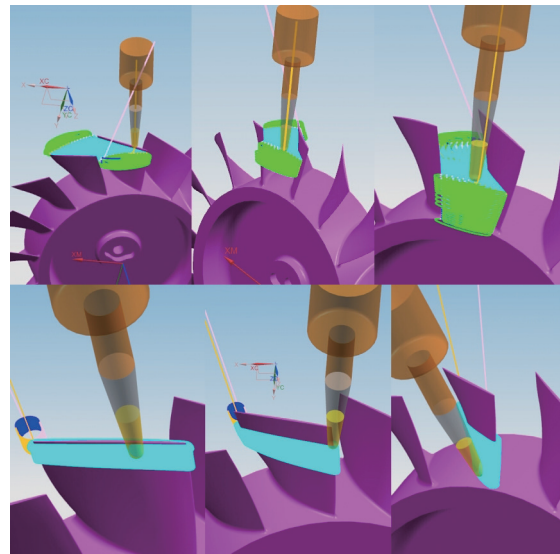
叶轮叶片粗加工/精加工刀具轨迹规划图
